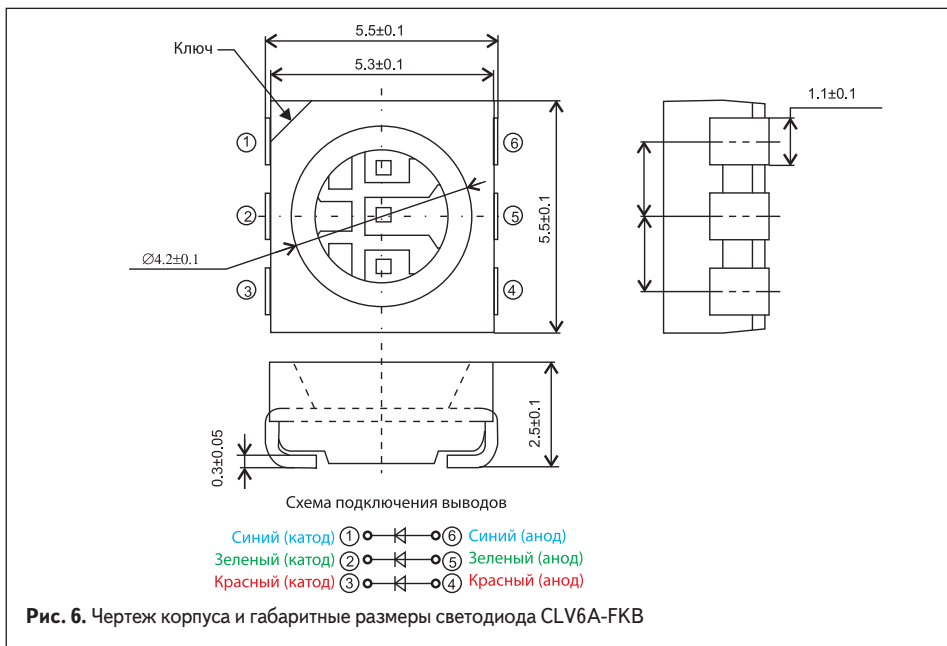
Чертеж корпуса и габаритные размеры светодиода CLV6A-FKB
